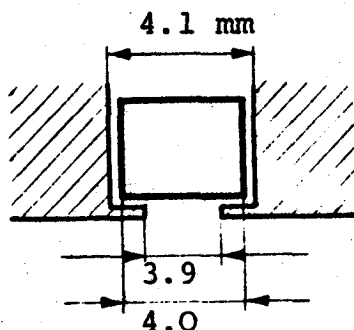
Teilansicht eines Längsschnittes durch die Matrize mit einem Katalysatorzylinder.
